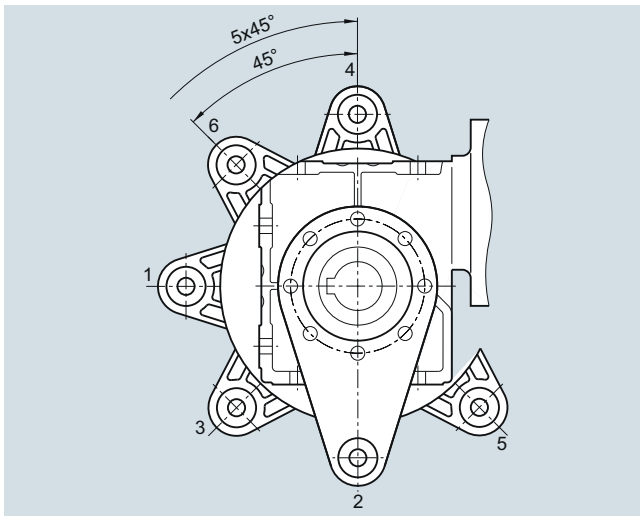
/13 Schneckengetriebe S in Aufsteckausführung
